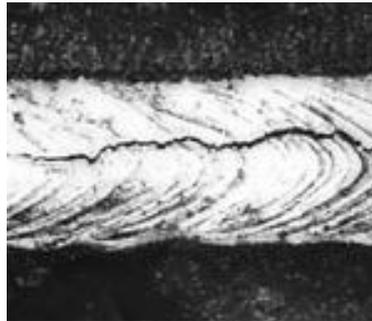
Defectos lineales en cordón de soldadura.
